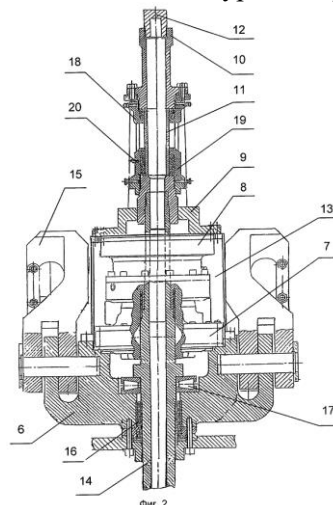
Верхний привод: 1 – вертлюг, 2 – параллелограмный механизм, 3 – каретка, 4 – направляющие, 5 – механизм подачи бурильных труб, 6 – корпус, 7 – гидромотор, 8 – тормоз, 9 – верхняя крышка, 10 – гусак, 11 – быстросменный уплотнительный узел, 12 – заглушка, 13 – кожух, 14 – выходной полый вал, 15 – штропы, 16 – игельчатые подшипники, 17 – упорный подшипник, 18, 19 – верхняя и нижняя гайки, 20 – манжеты
